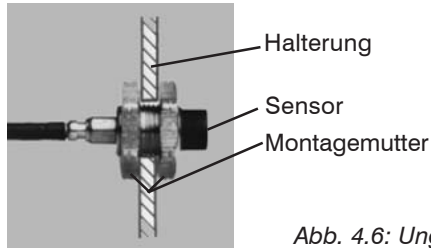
Ungeschirmter Sensor mit Gewinde in Standardmontage
